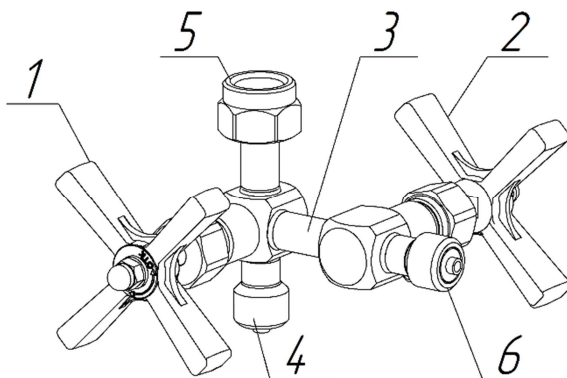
Конструктивная схема изделия: 1 – вентиль запорный; 2 – вентиль дренажный; 3 – трубка соединительная; 4 – входной штуцер; 5 – выходное присоединение; 6 – дренажный штуцер
